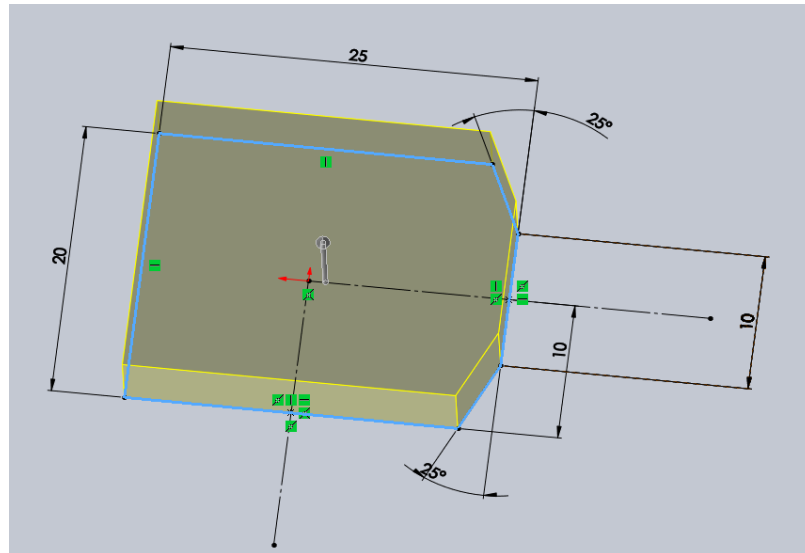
Extrusión desde su croquis hasta una altura de 5mm.
